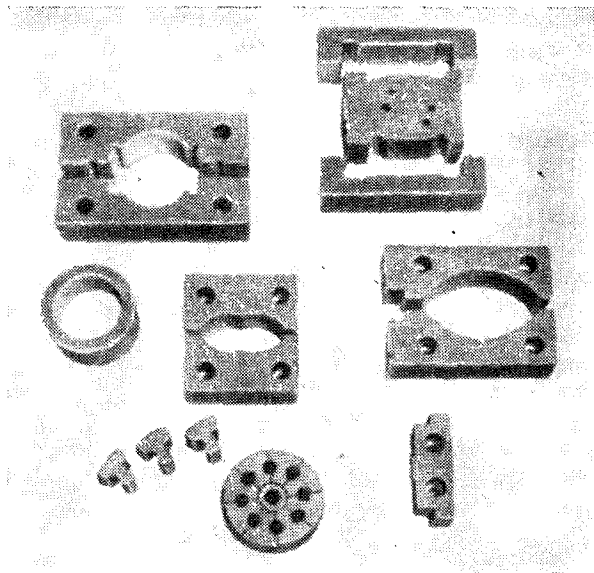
Твердосплавные части штампа для вырубки деталей из листовой стали для статоров и роторов электродвигателей
